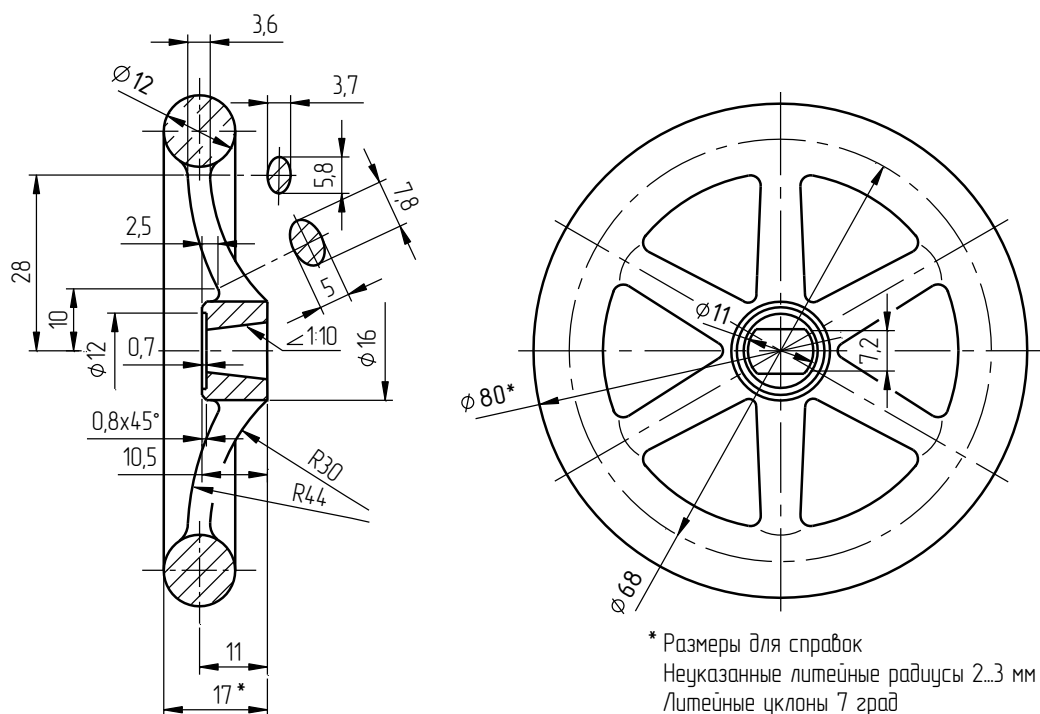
Чертеж детали (маховичек вентиля), в котором необходимые изображения (разрез и вид слева) выполнены полными – без сокращений
